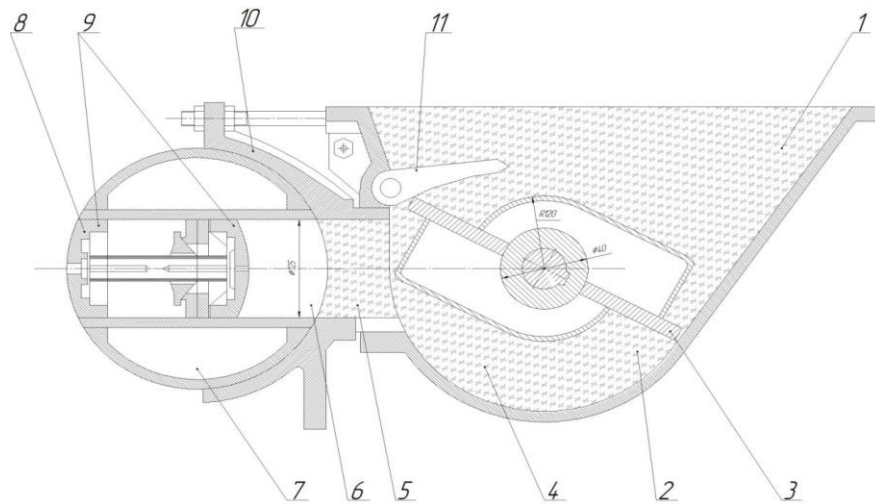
Конструкція модернізованої робочої камери:
